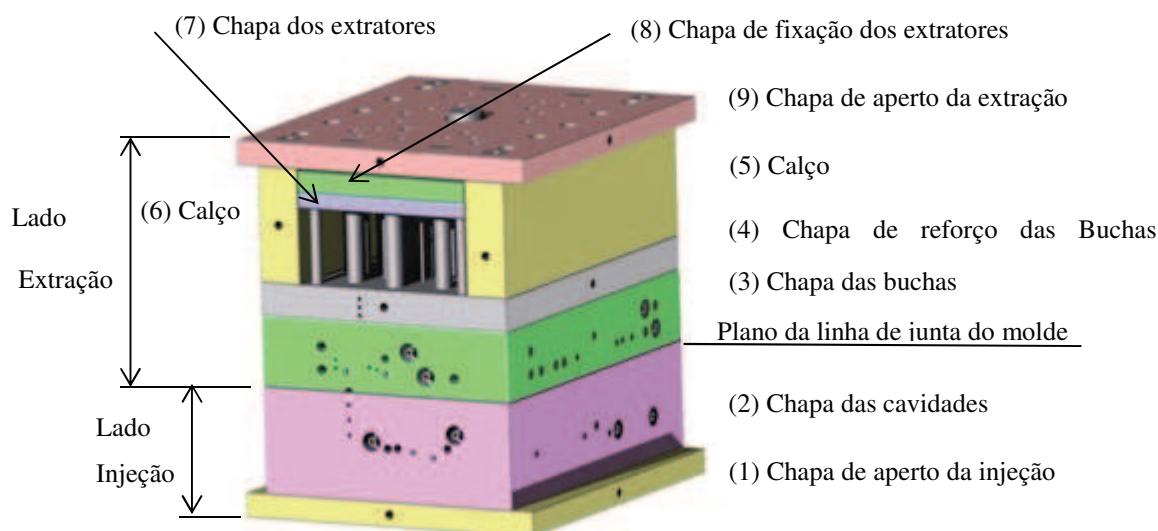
Molde de injeção: estrutura (parte fixa e móvel).
